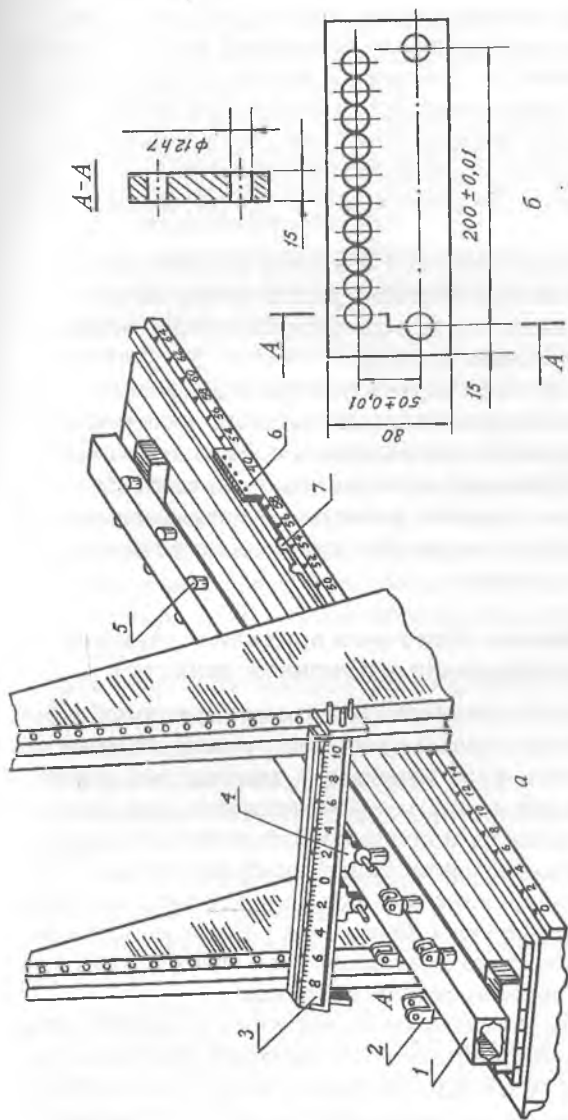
Монтаж балки в инструментальном стенде: 1 — заливка вилок в стаканы; 2 — балка приспособления; 3 — вилка фиксатора, залитая цементом; 4 — поперечная координатная линейка; 5 — переходной фитинг; 6 — стакан, приваренный к балке приспособления; 7 — дистанционный калибр; 8 — дистанционный фитинг; 9 — конструкция постоянного дистанционного калибра
